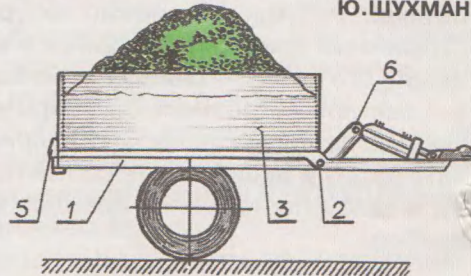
1 — рама прицепа; 2 — шарнир, соединяющий части кузова; 3 — короб, образованный бортами; 5 — замки; 6 — рычаг рамы.
